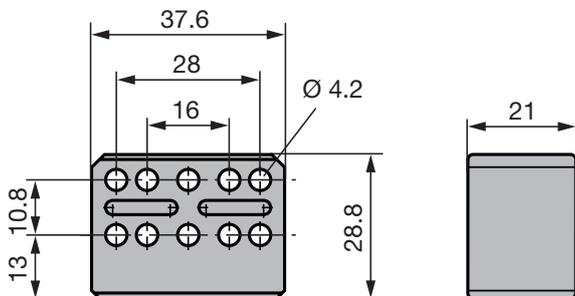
Dimensions de montage du capteur de position BTL6-A-3800-2
